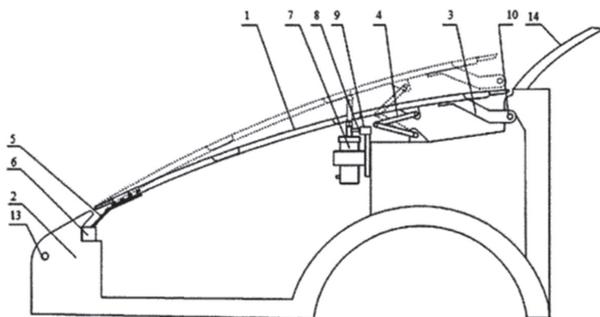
Общий вид активного капота сбоку: 1 – крышка капота; 2 – рама; 3 – кронштейны крепления задней части капота; 4 – рычажная система; 5 – петля; 6 – защелка; 7 – пневмоцилиндры; 8 – фиксаторы штока; 9 – электромагнит; 10 – пальцы крепления рычагов 4; 13 – контактный датчик; 14 – передние стойки рамы лобового стекла
